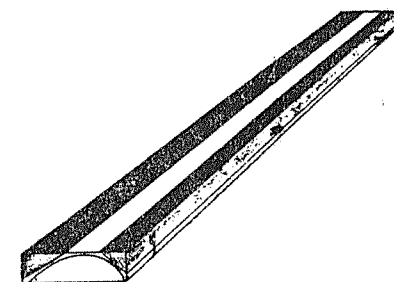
Шаблон для изготовления передней кромки крыла.
